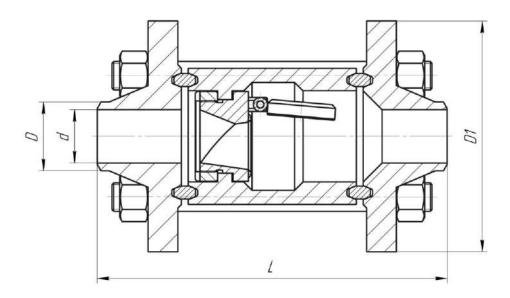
Общий вид затвора с номинальным давлением Ру>6,3 МПа
